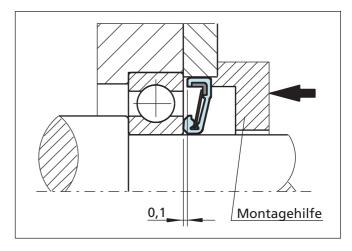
Einbau der Axial-Wellendichtung mit Montagehilfe
